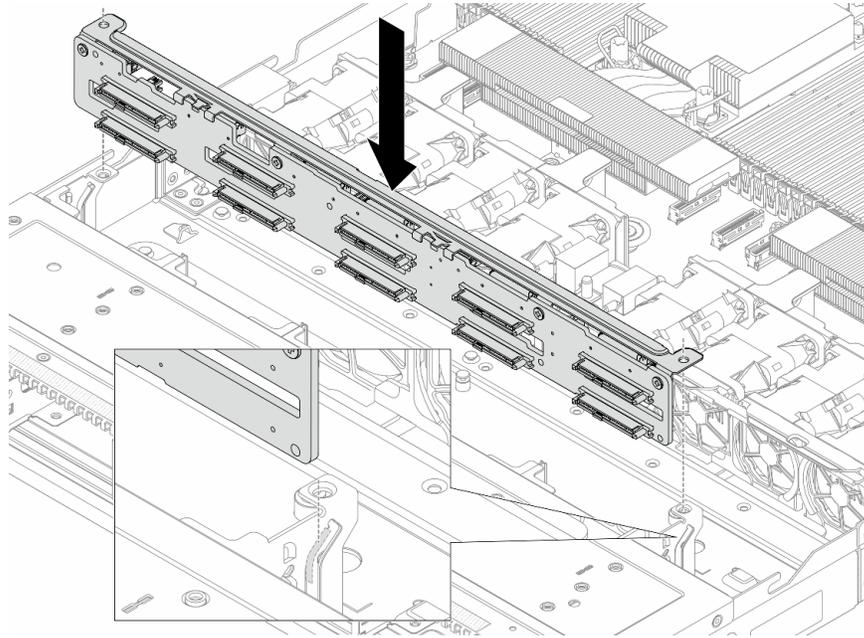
Installation du fond de panier pour dix unités remplaçables à chaud 2,5 pouces
